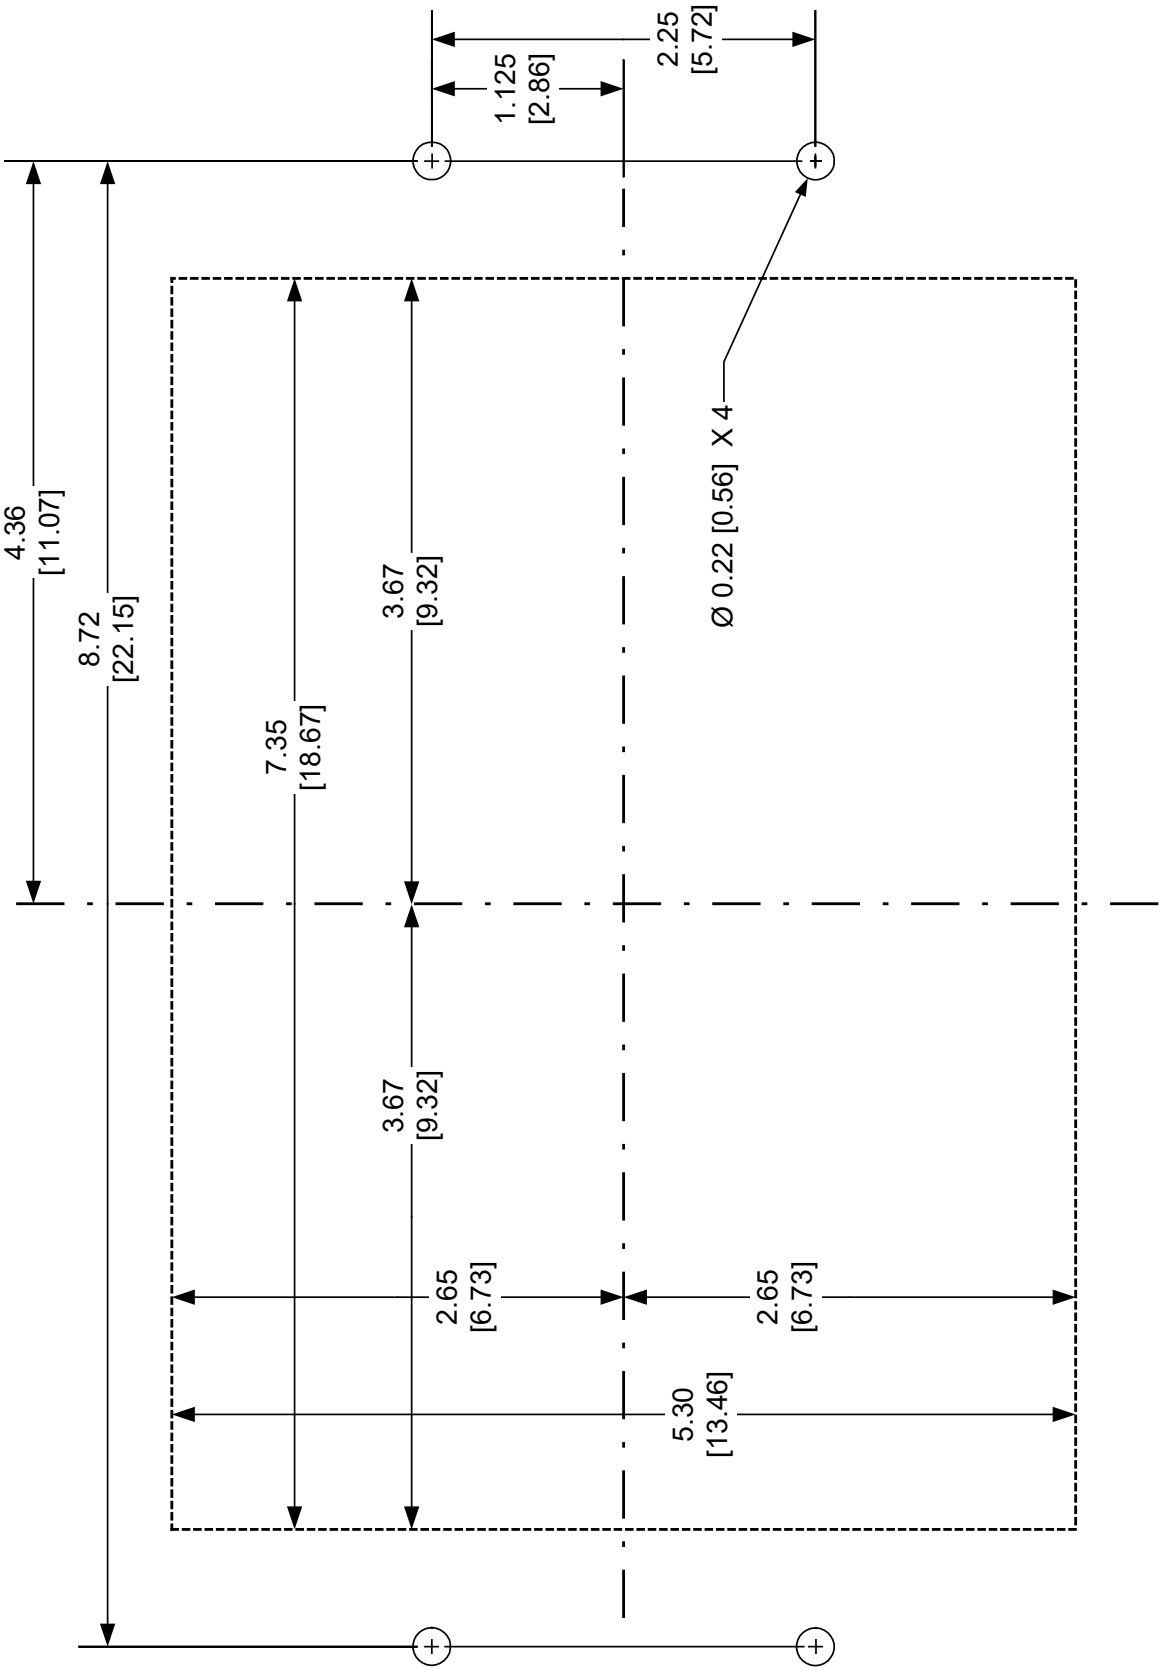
M-7679 Dimensiones de Corte del Panel Horizontal
